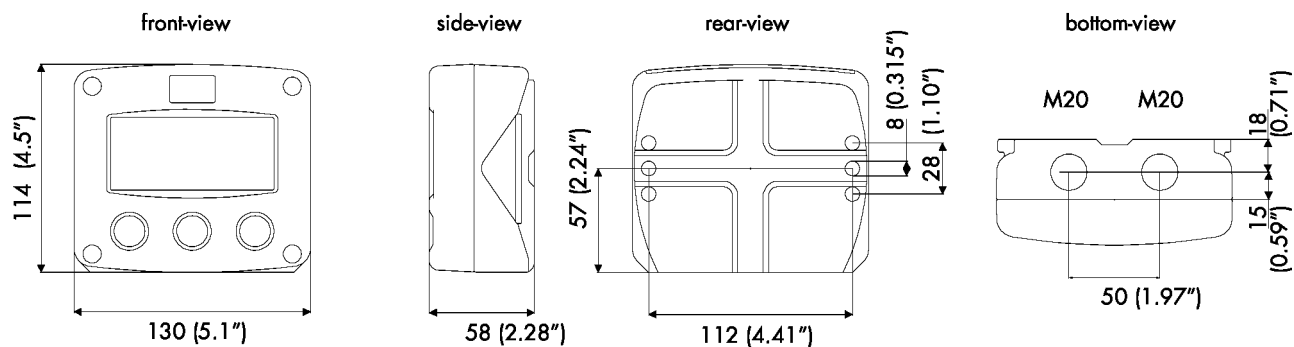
Abmessungen für IP67/NEMA 4X Aluminiumgehäuse (MTL661)
